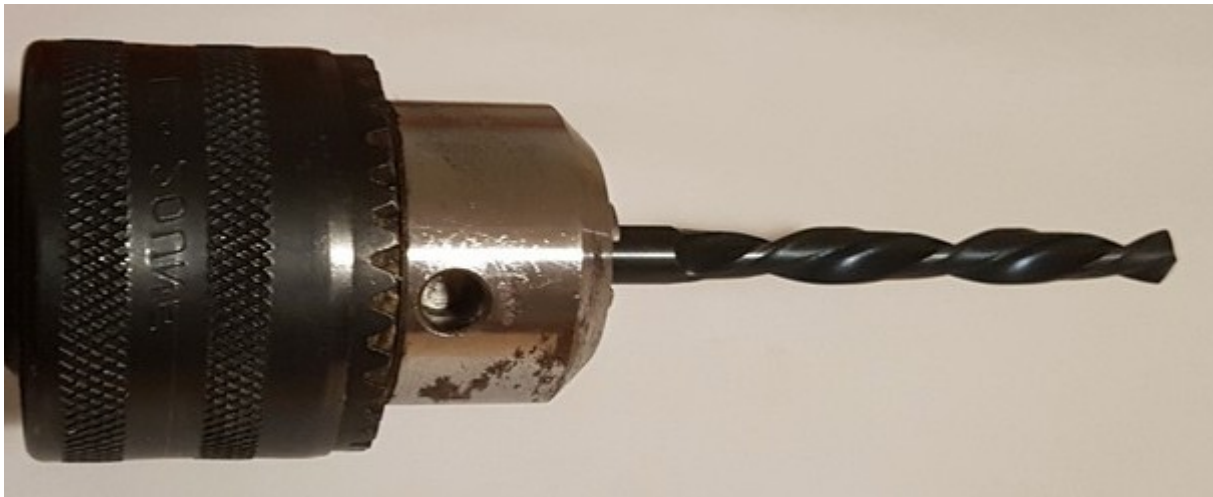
Bohrfutter mit Werkzeug einer Bohrmaschine
